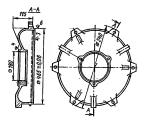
Подшипниковый щит асинхронного двигателя,
